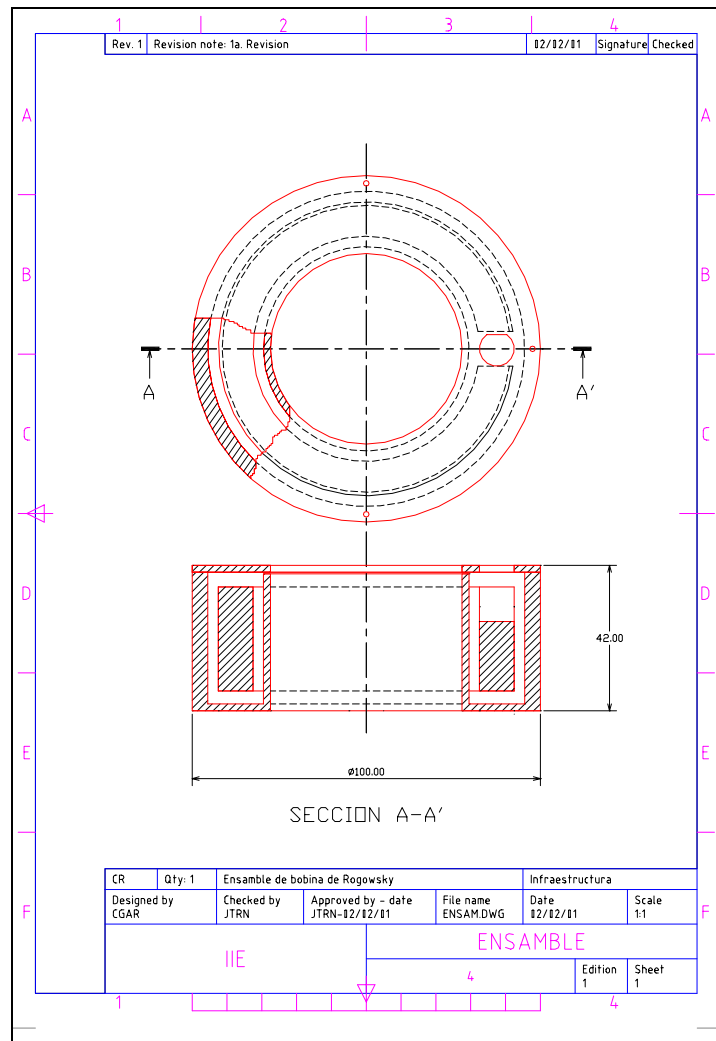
14 Dibujo de conjunto del sensor desarrollado
